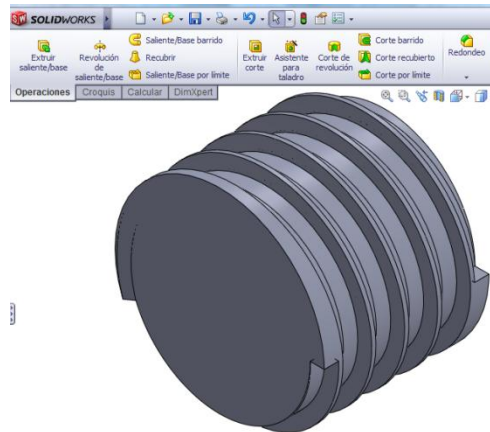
Diseño de la pieza de fresado en SolidWorks.
